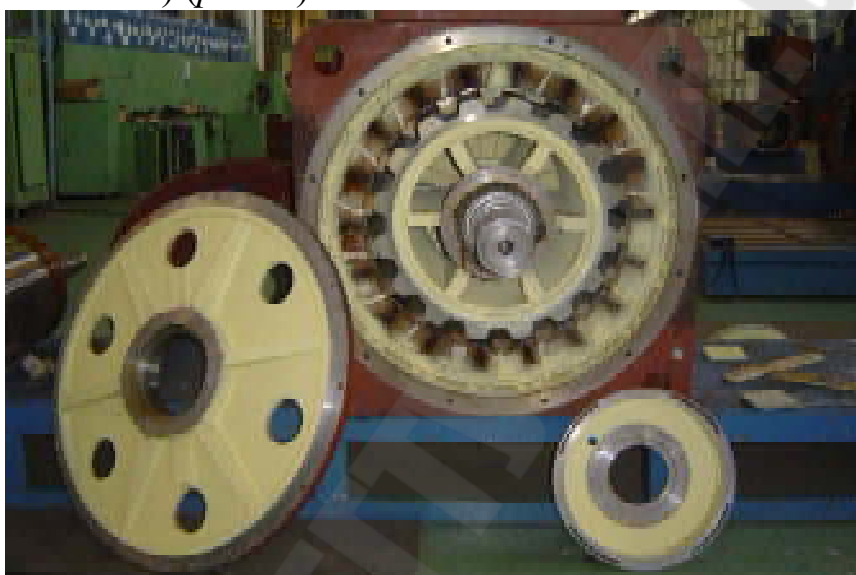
Внешний вид вентильно-индукторного двигателя
